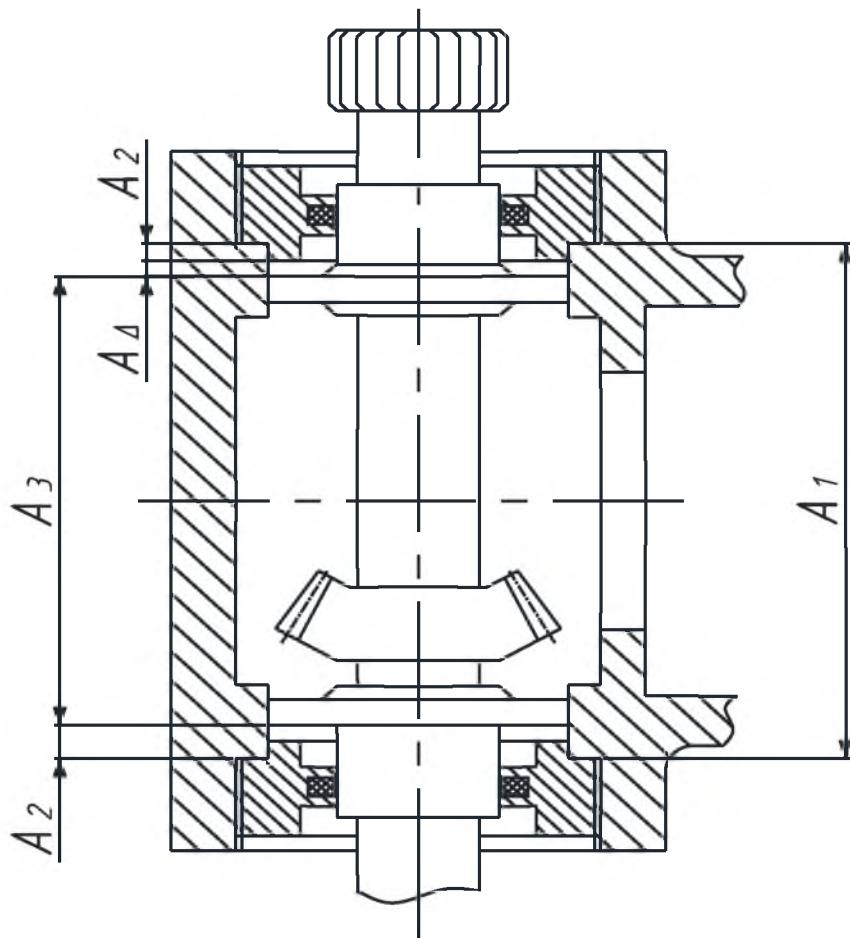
Эскиз узла редуктора винтового подъемника
